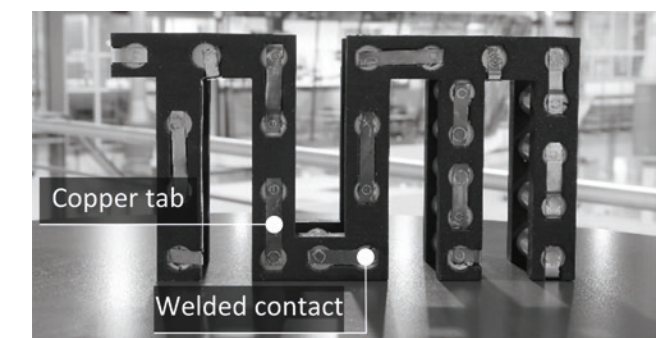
Demonstrator eines mit grüner Laserstrahlung geschweißten Batteriepacks
